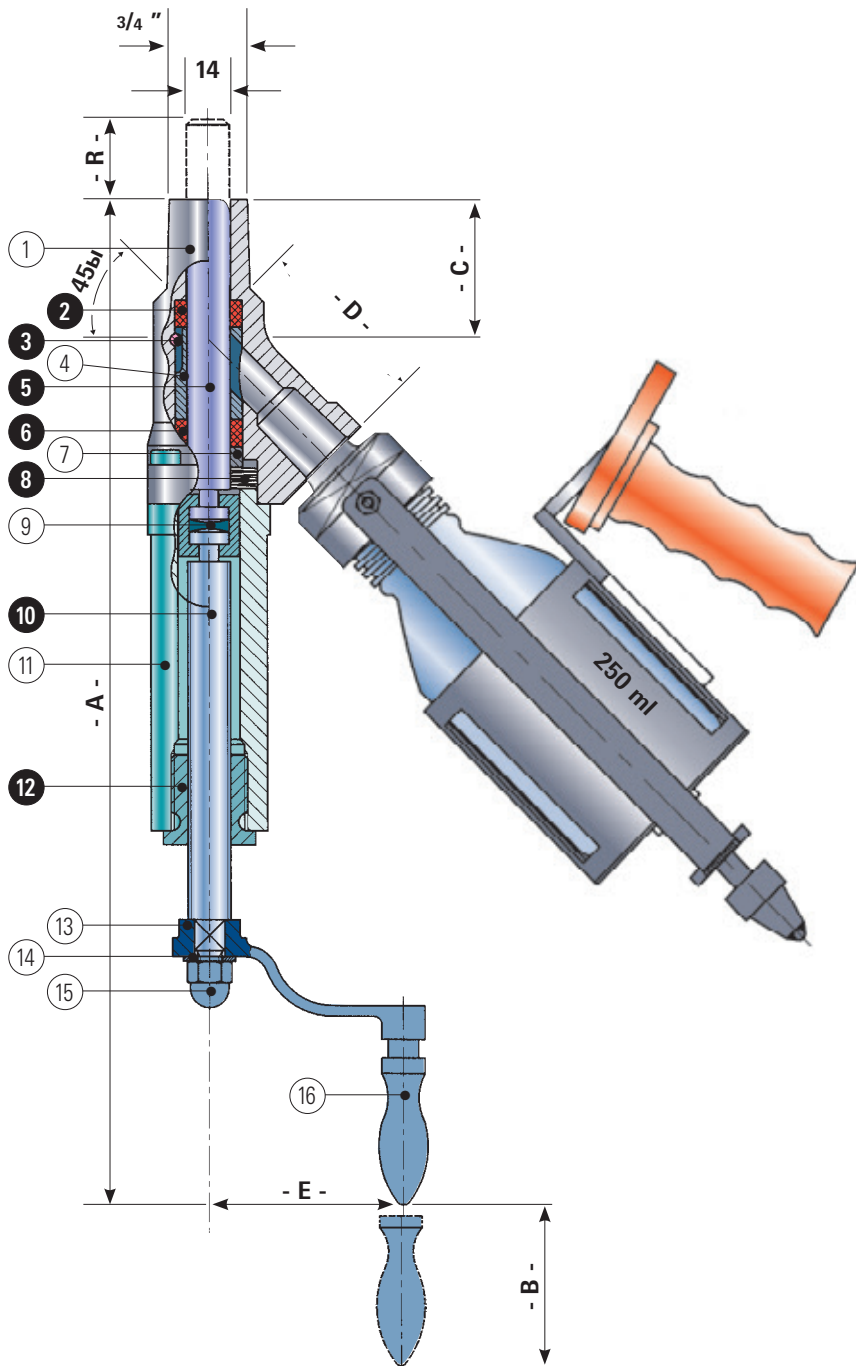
Yarway 1/2" Sample Valve with bottle holder
